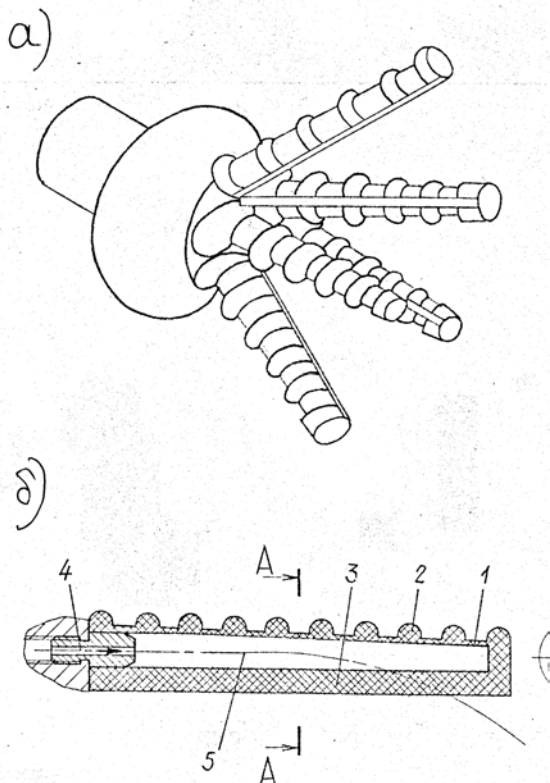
Пневматический схват с пятью гибкими надувными пальцами: а – внешний вид; б – разрез пальца:
